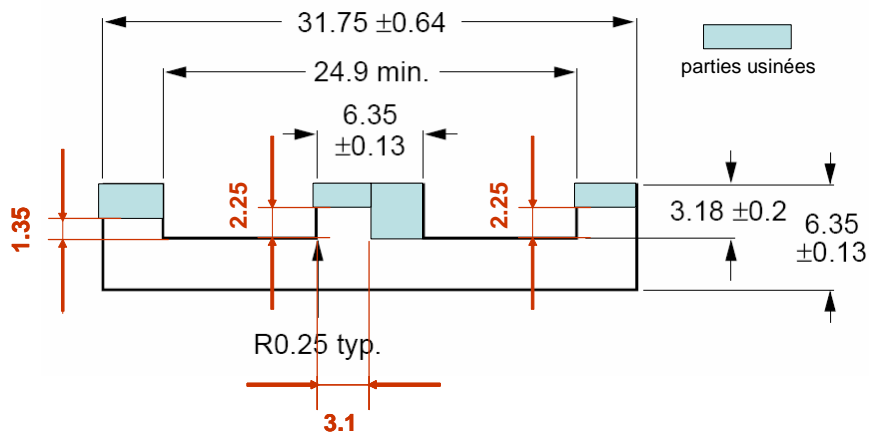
Usinage du noyau magnétique de prototype B (E32/3/20)
